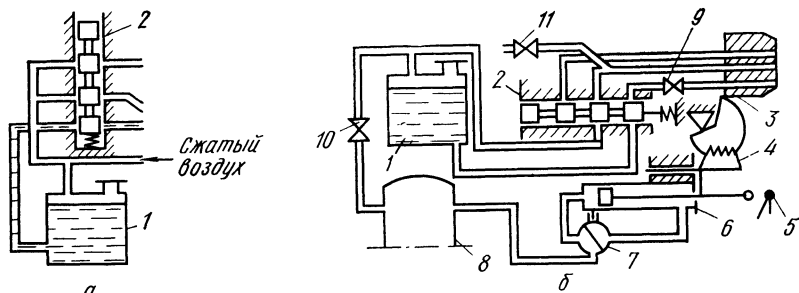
Схемы устройств для подачи смазки при помощи ручного пистолета [147]
